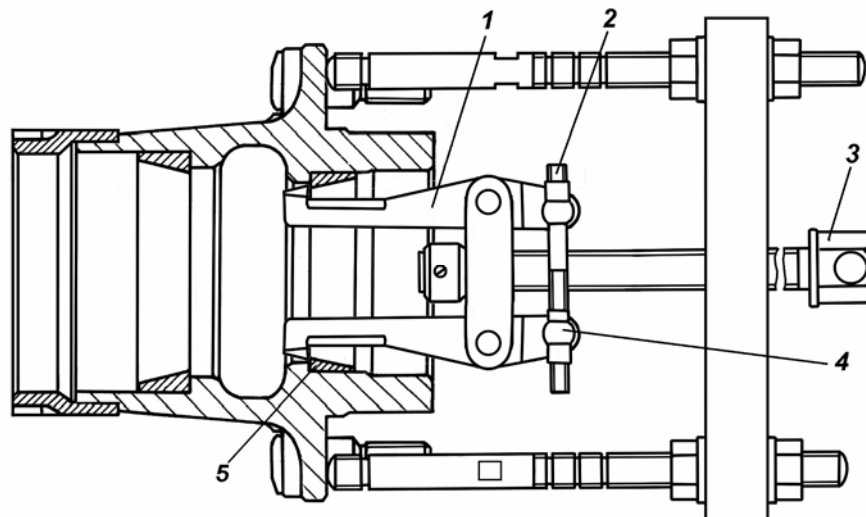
Выпрессовка наружных колец подшипников: 1 – лапки, 2 – болт, 3 – винт; 4 – ось; 5 – кольцо подшипника
